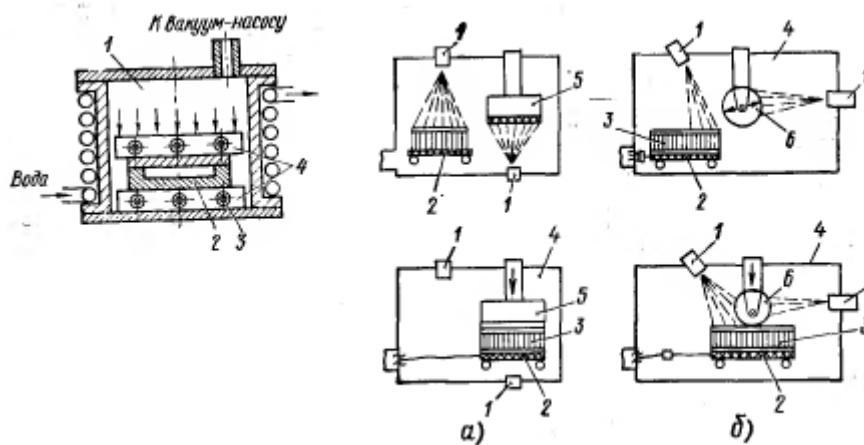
Схема сварки конструкции из титановых сплавов в твердом состоянии с использованием сверхпластичности:
